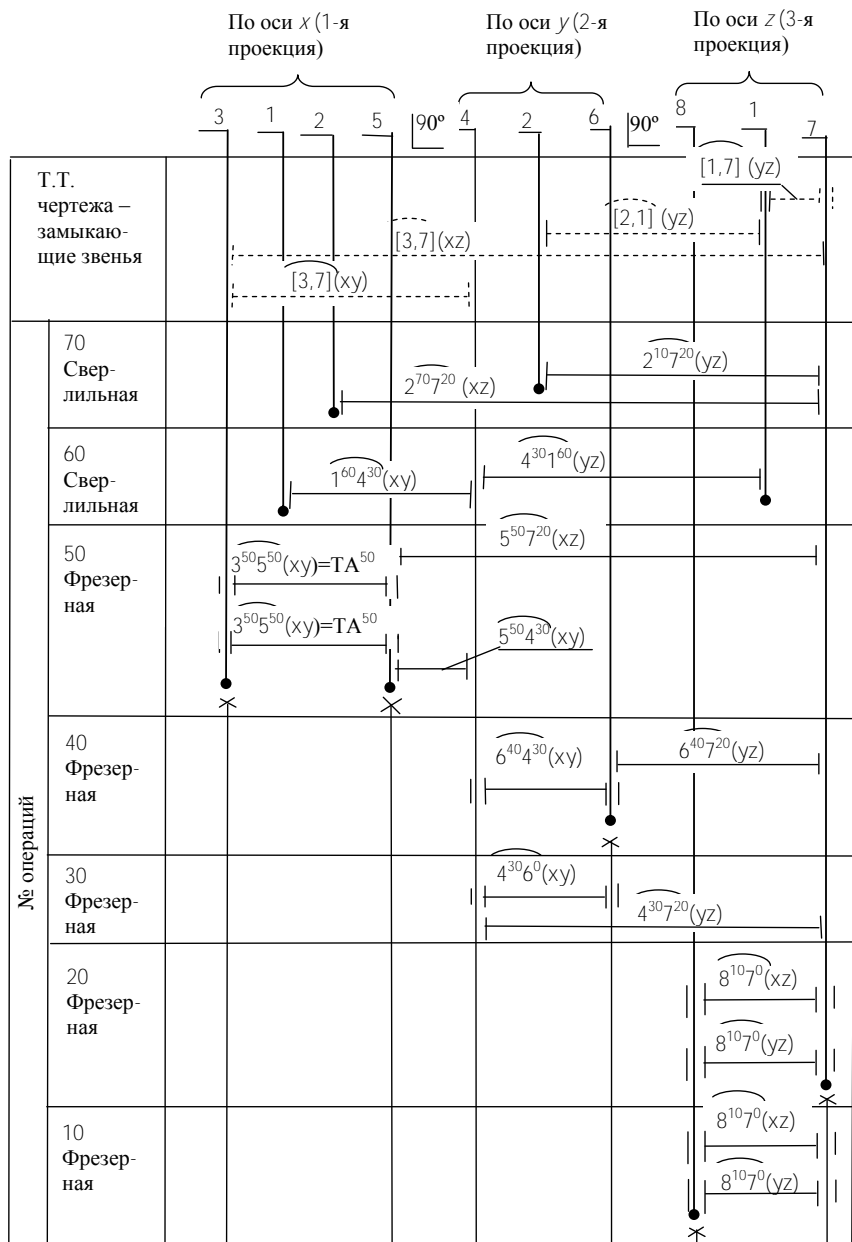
Схема пространственных отклонений поверхностей корпусной детали
